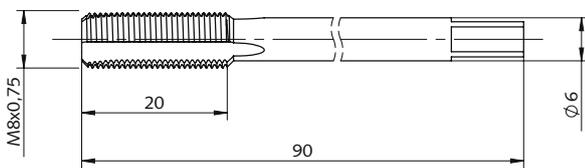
Gewindebohrer M8x0,75 Typ 1361
